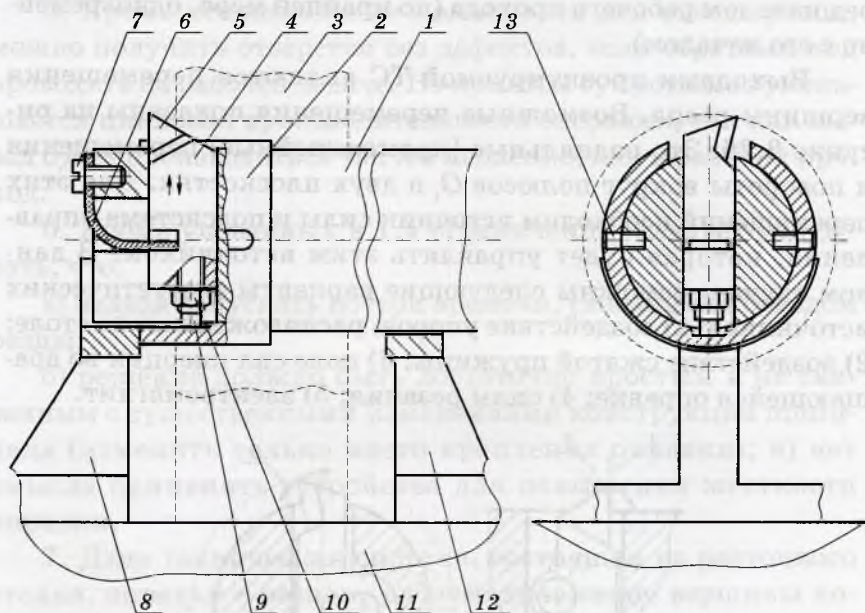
Схемы возможных способов перемещения вершины резца:
